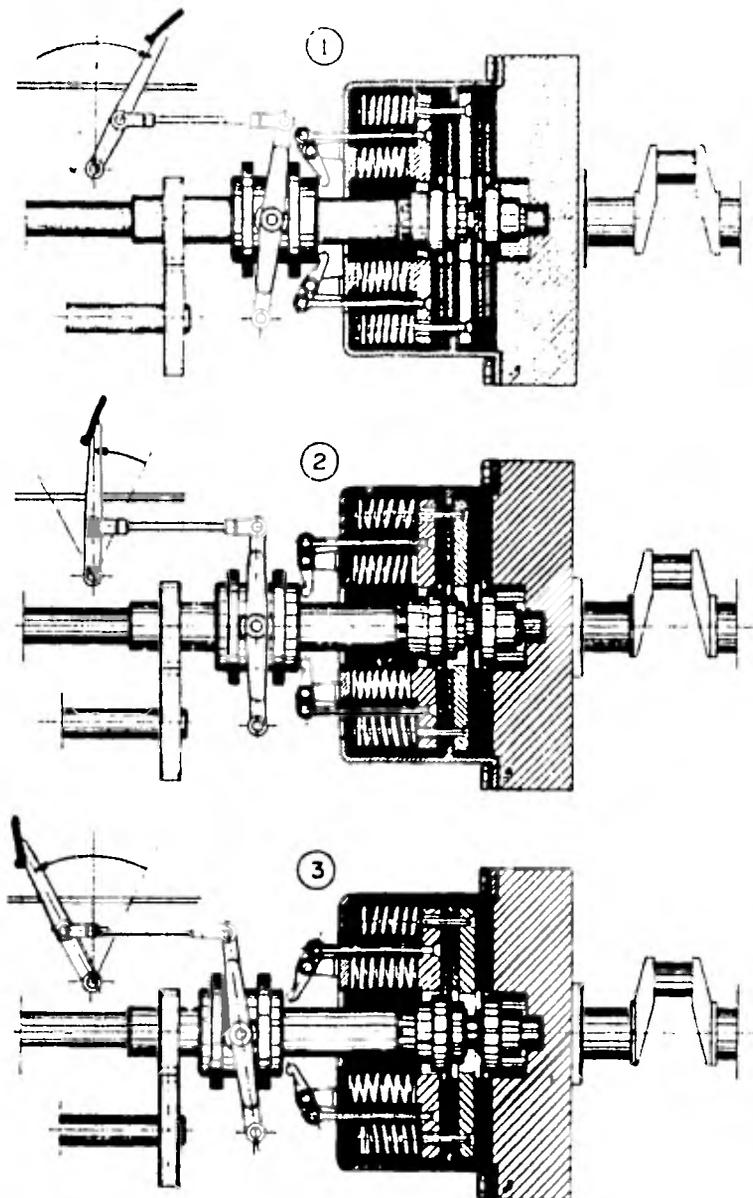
4 Tres posiciones del embrague de doble acción.
